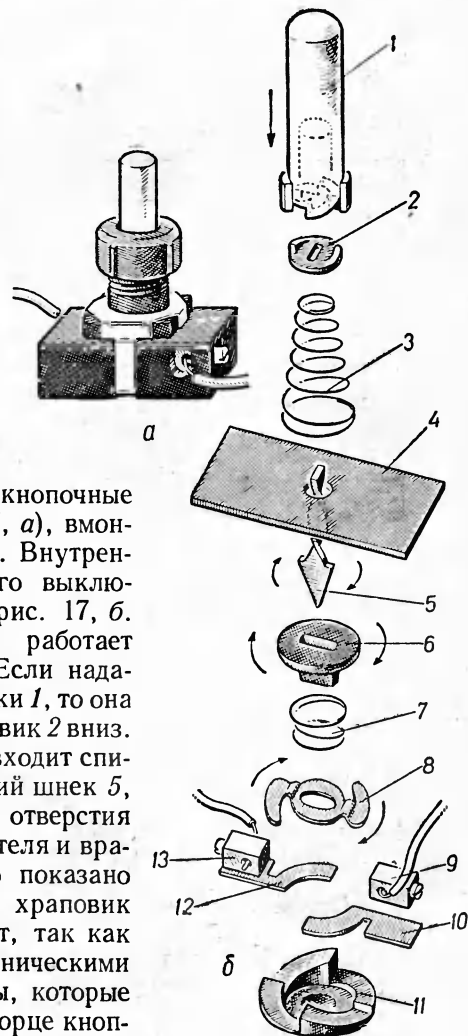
Внешний вид (а) и устройство (б) кнопочного выключателя.
